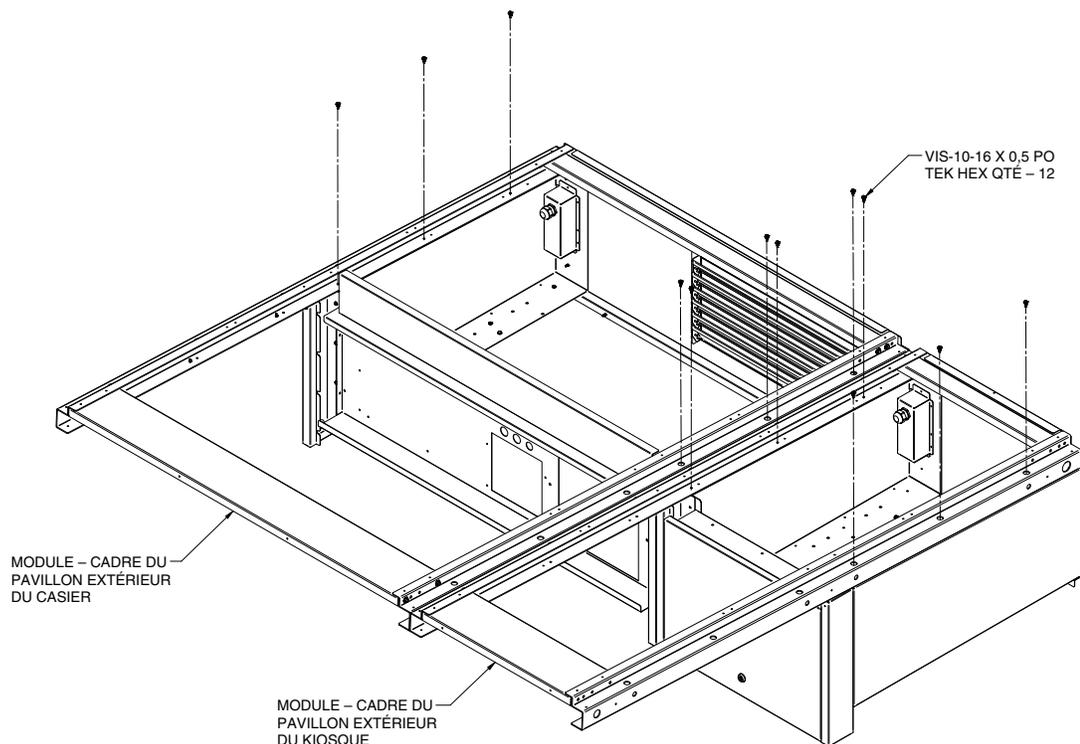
Vue supérieure des cadres de pavillons fixés au module réfrigéré et au kiosque de contrôle
